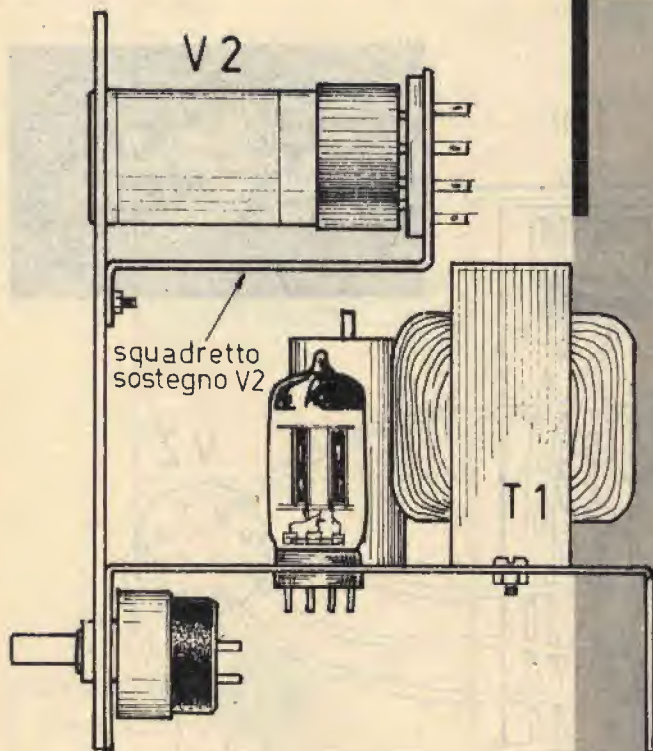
Questo disegno illustra il montaggio meccanico dei vari componenti sul telaio metallico.
